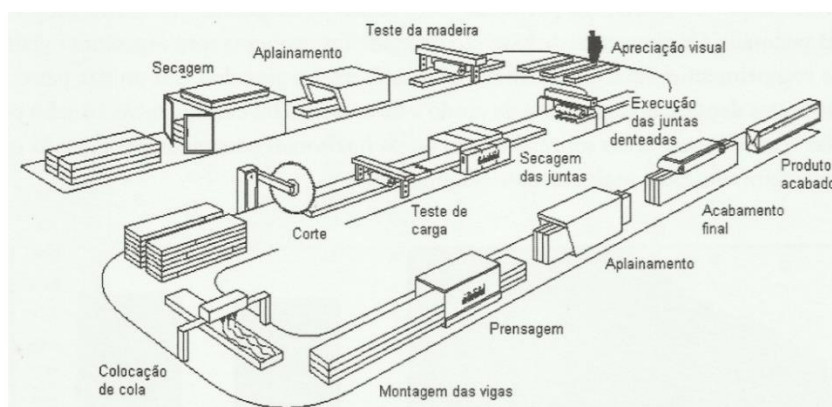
Fases da produção da Madeira Lamelada Colada (Cachim, P., 2007)
